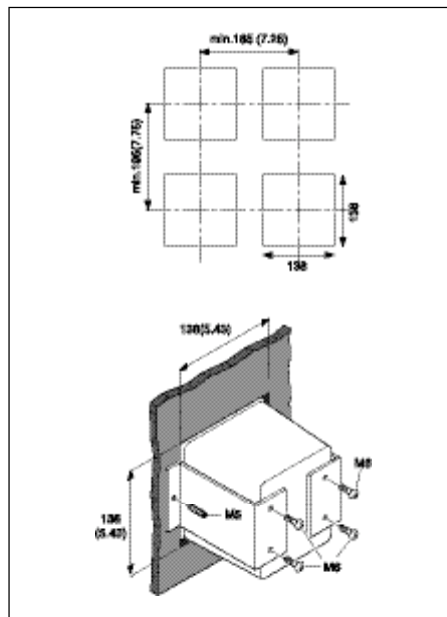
Option /UM kit de montage universel, schéma de montage sur panneau
